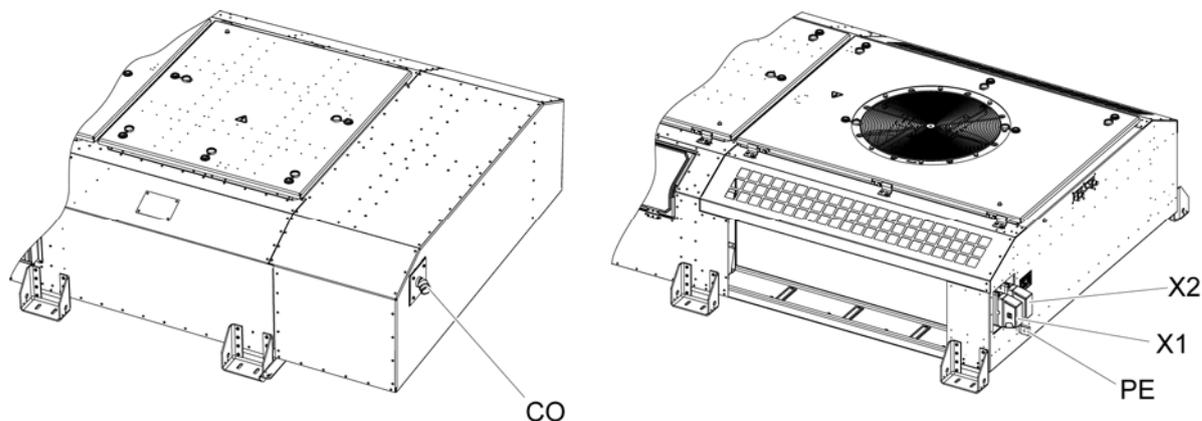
Chiusura accesso al riscaldatore cabina di guida
